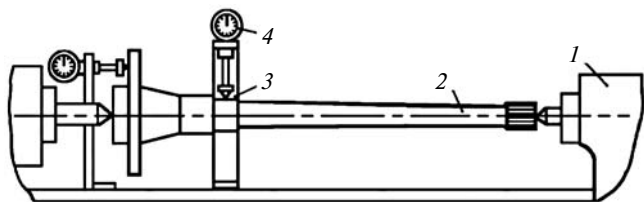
Установка полуоси для определения биения вала и торца фланца: 1 — прибор ПБ-1400; 2 — полуось; 3 — стойка индикатора; 4 — индикатор ИЧ-10 ГОСТ 577
